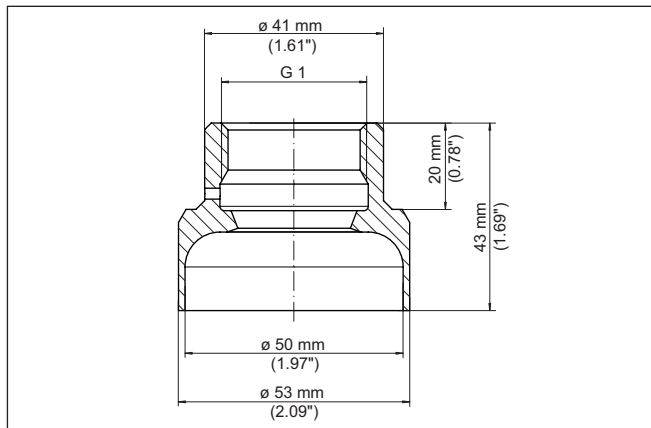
Dimensions raccord à souder direct pour montage sur tube G1 - Joint conique
